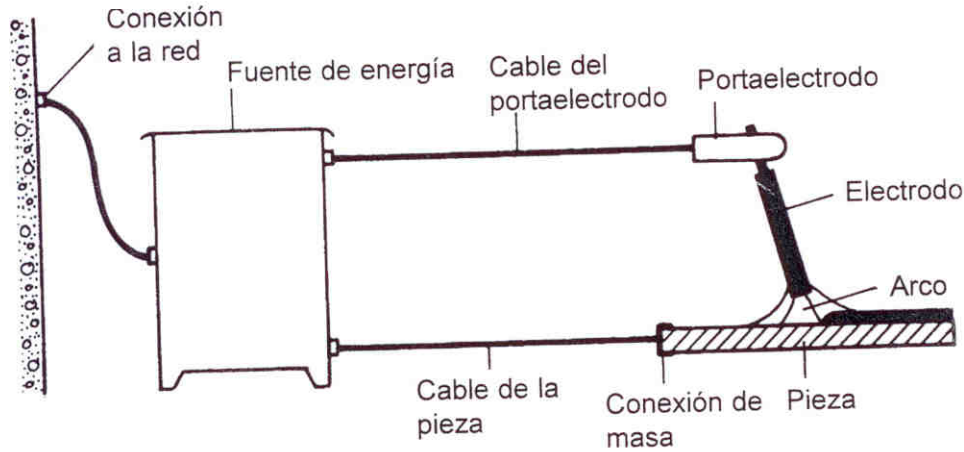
Esquema de una instalación para soldadura por arco.
